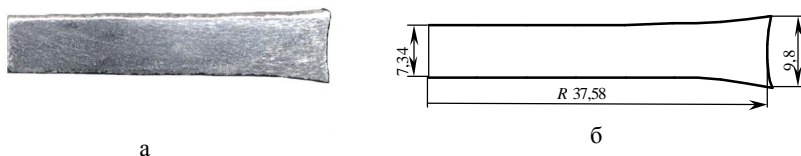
Сечение СВС-спрессованной заготовки из сплава TiC-20% Ni:
